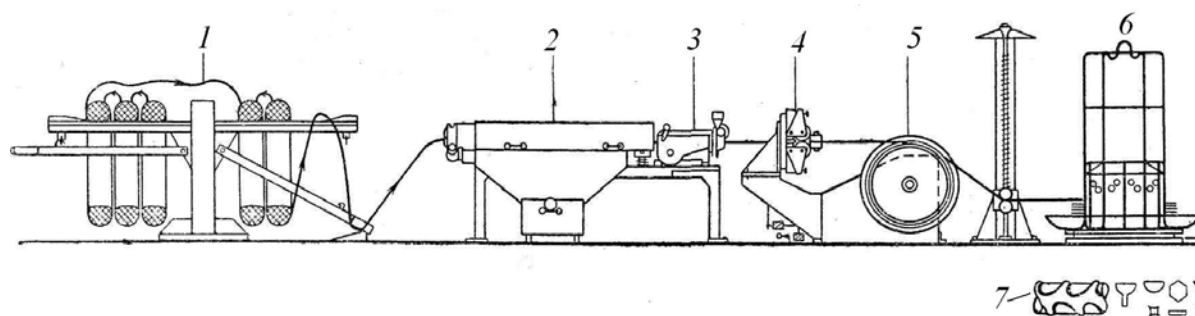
Схема поточной линии для механической очистки, волочения и профилирования проволоки: 1 – разматыватель; 2 – устройство для механического удаления окалины; 3 – волокодержатель; 4 – профилирующий аппарат; 5 - волочильный барабанный стан; 6 – намоточное устройство; 7 – образцы профилей, изготовляемых на данной линии.
